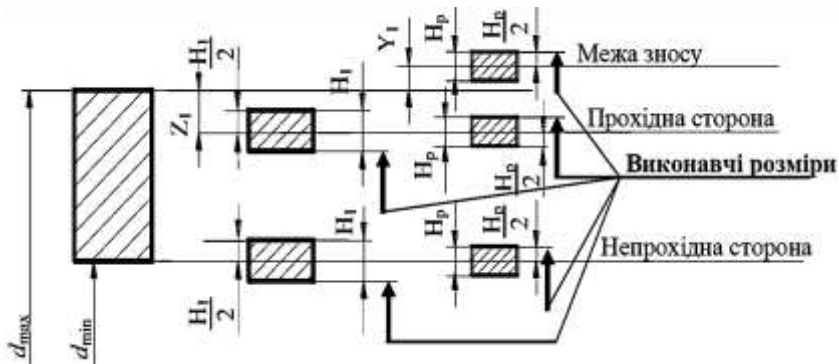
Схема розташування полів допусків калибрів-скоб для контролю валів розміром до 180мм 6-8 квалітетів точності
